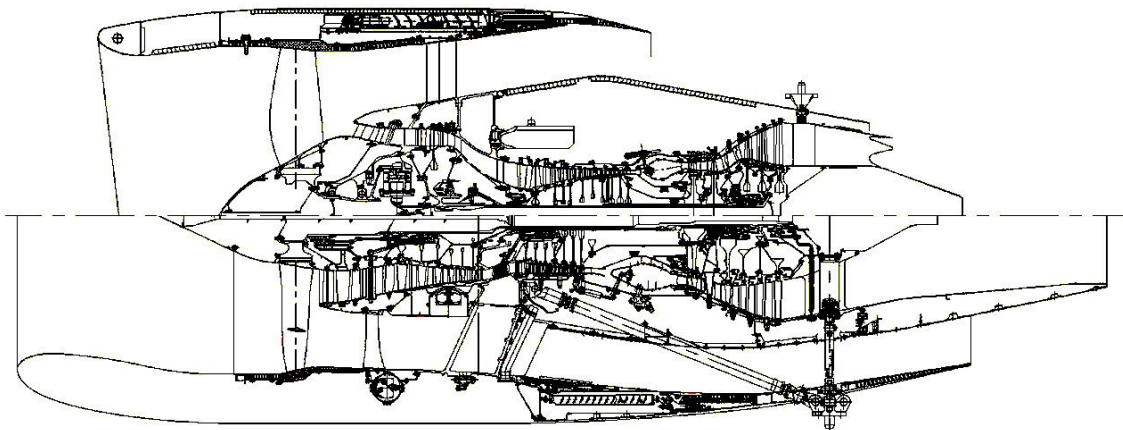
Схемы ТРДД с редуктором и без редуктора
